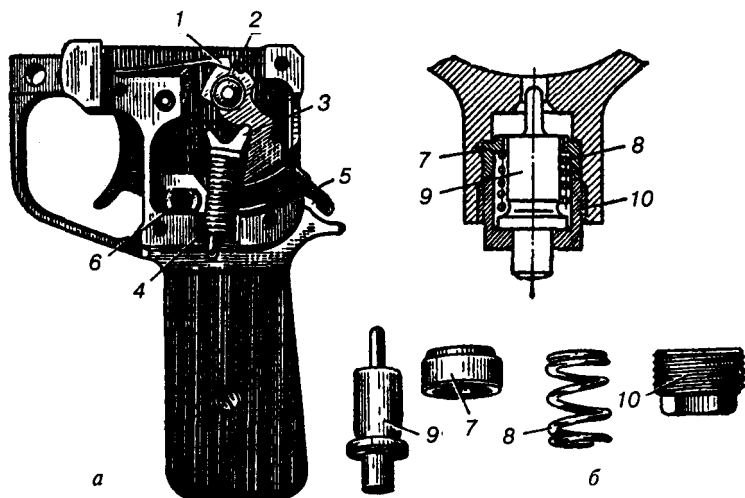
Ударно-спусковой и бойковый механизмы РПГ-7:
